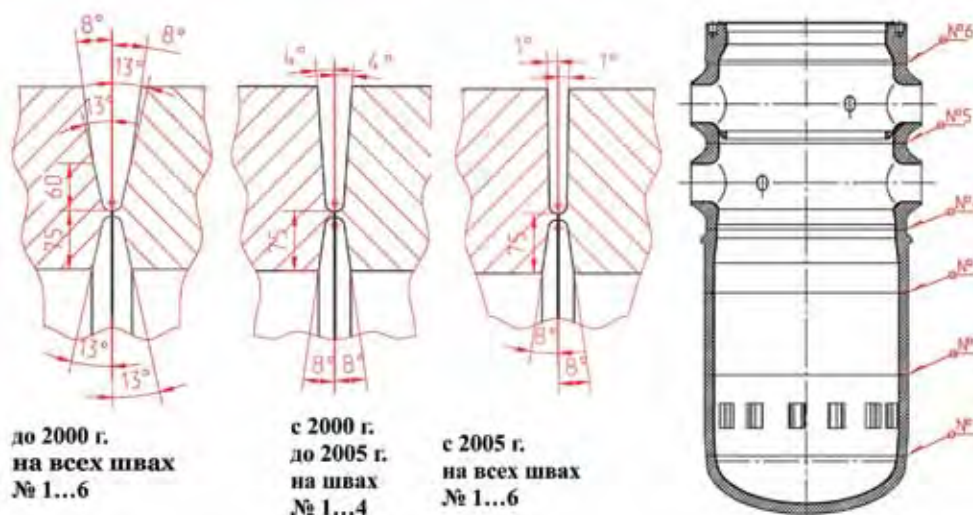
Развитие технологии сварки кольцевых швов корпуса реактора ВВЭР-1000
